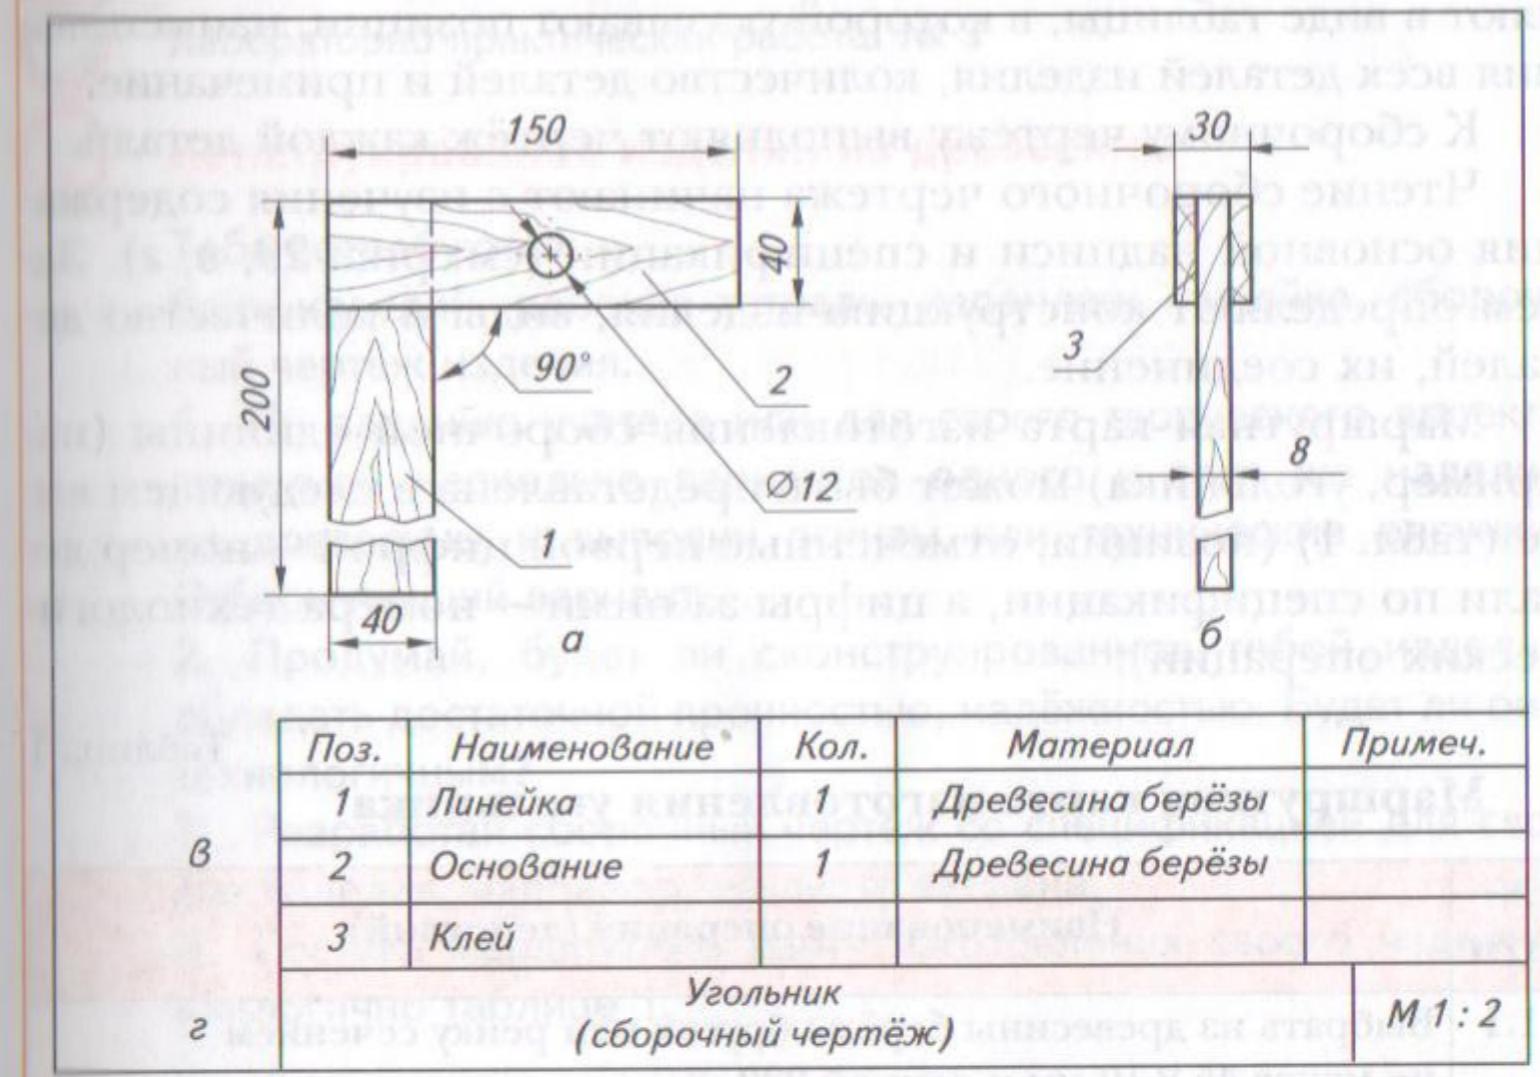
Сборочный чертёж угольника: а — главный вид; б — вид слева; в — спецификация; г — основная надпись
